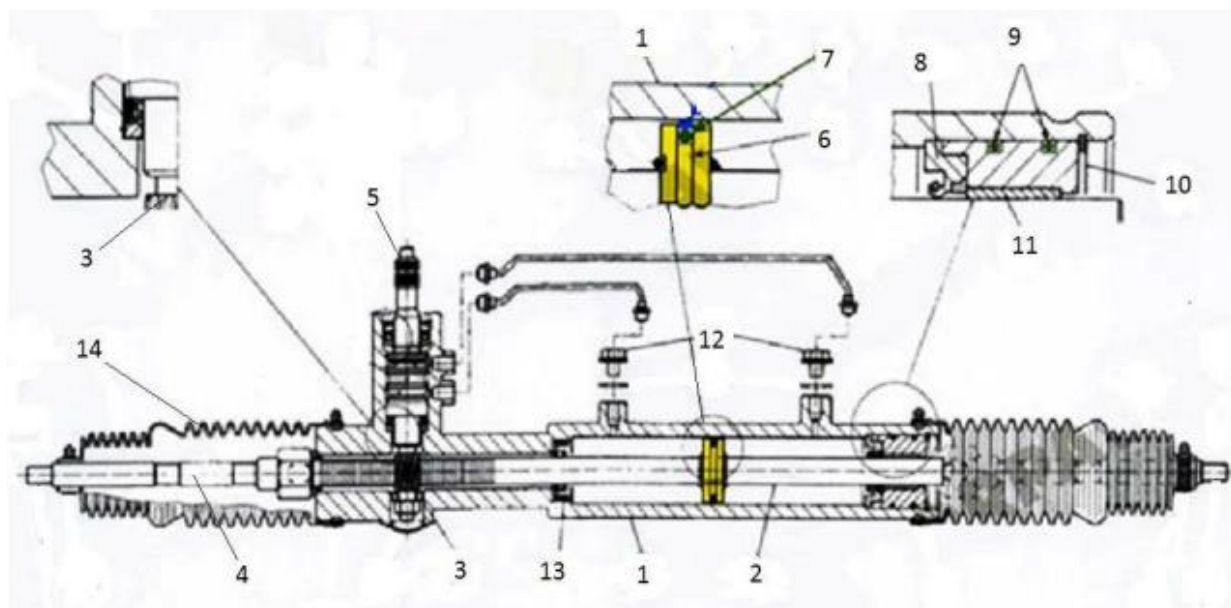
Рейковий рульовий механізм із гідропідсилювачем: 1 - корпус; 2 - шток-рейка; 3 - шестерня; 4 - рульова тяга; 5 - шліцьовий хвостовик тангенціального золотника; 6 - поршень силового циліндра; 7 - ущільнення поршня; 8 - корпус ущільнення штока; 9 - кільця ущільнювачів; 10 - стопорне кільце; 11 - втулка; 12 - штуцери сталевих трубок; 13 - ущільнення штока; 14 - гофрований чохол
